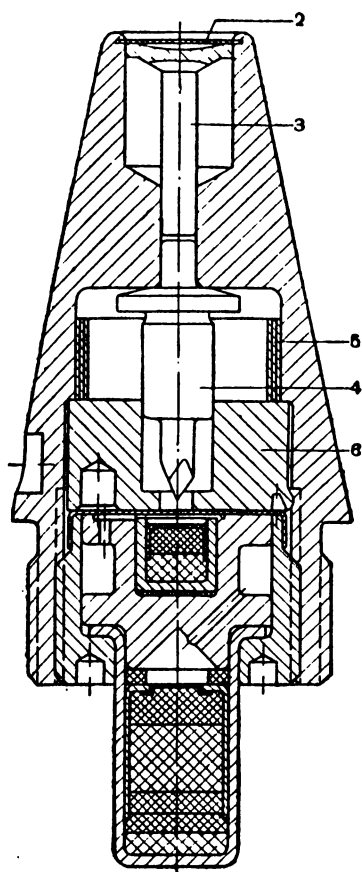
Взрыватель Б-23. Положение деталей в полете:
